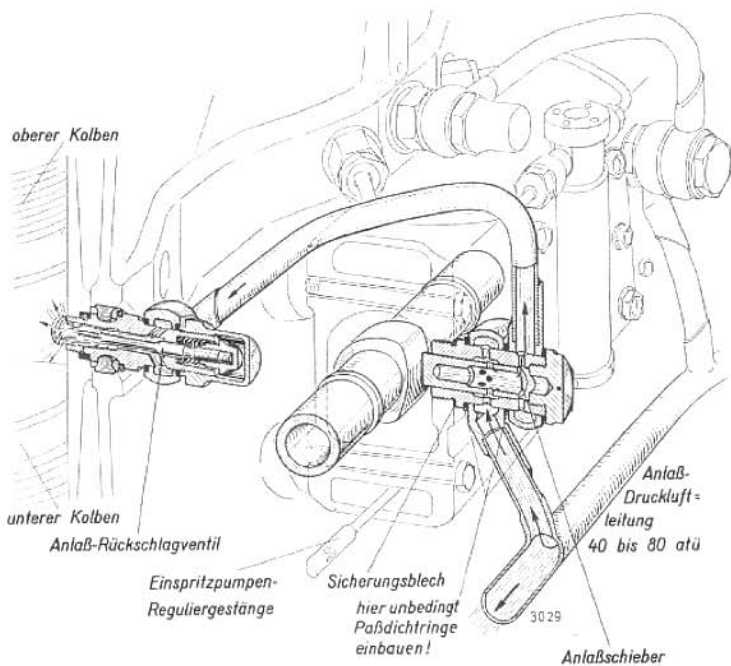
Zwangsläufige Steuerung der Anlaßluft am Motor
